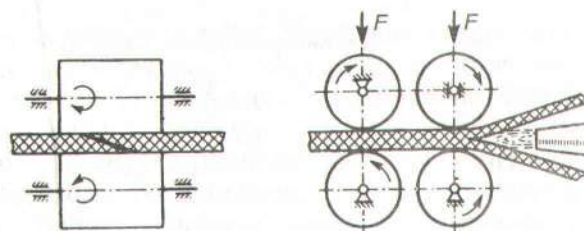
Зварювання нагрітим газом без присадкового матеріалу: F — сила стиску
